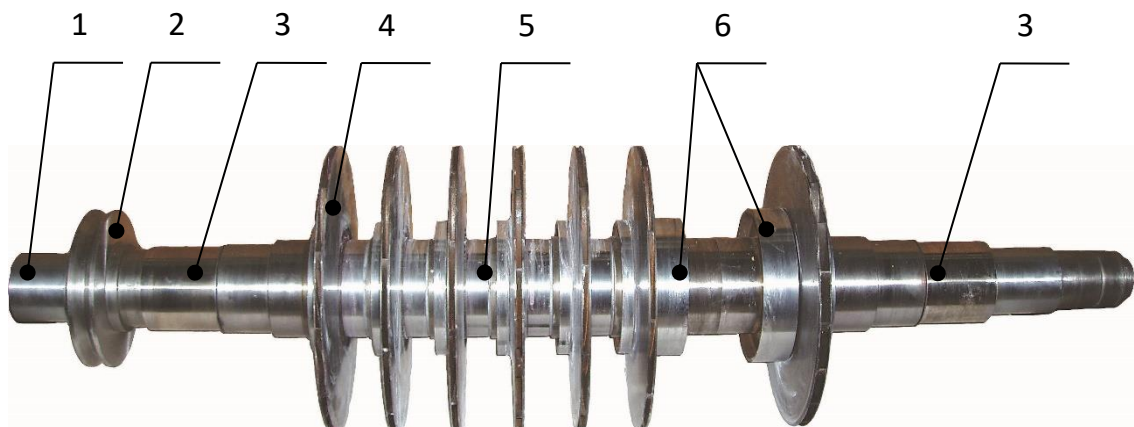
Ротор відцентрового компресора 401КВД
